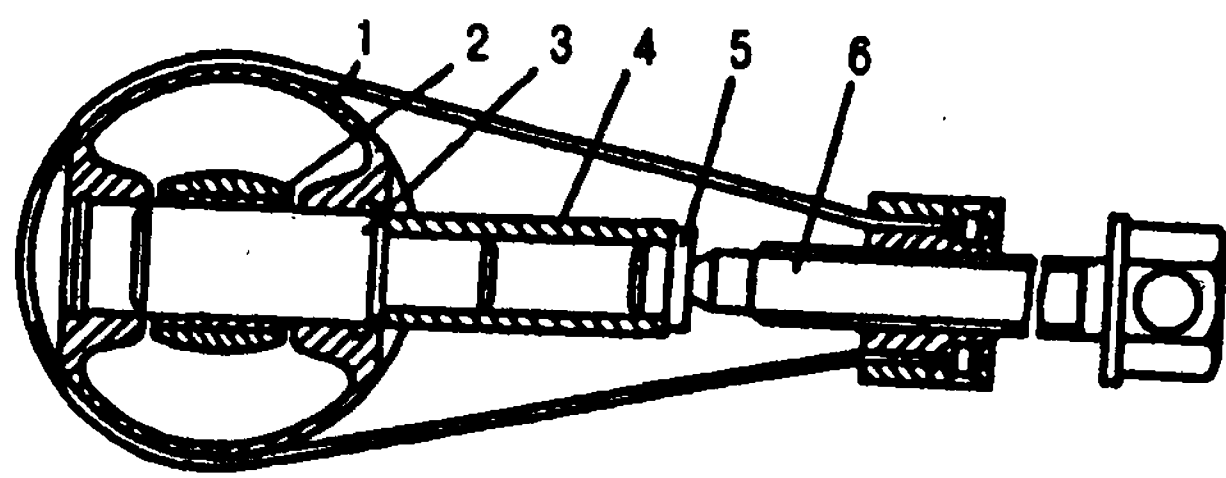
Запрессовка поршневого пальца в поршень и шатун с помощью приспособления: 1 - поршень; 2 - шатун; 3 - оправка; 4 - палец; 5 - подпятник; 6 - винт
